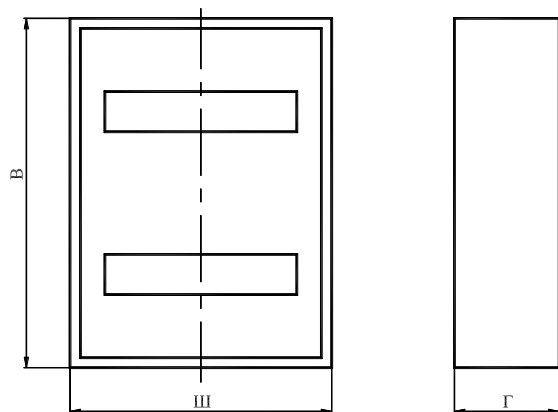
Габаритные размеры корпусов металлических ЩРН
